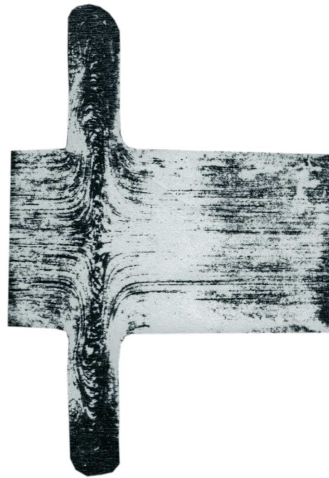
Desfășurarea fibrajului unei flanșe refumate cu partea de testare.
